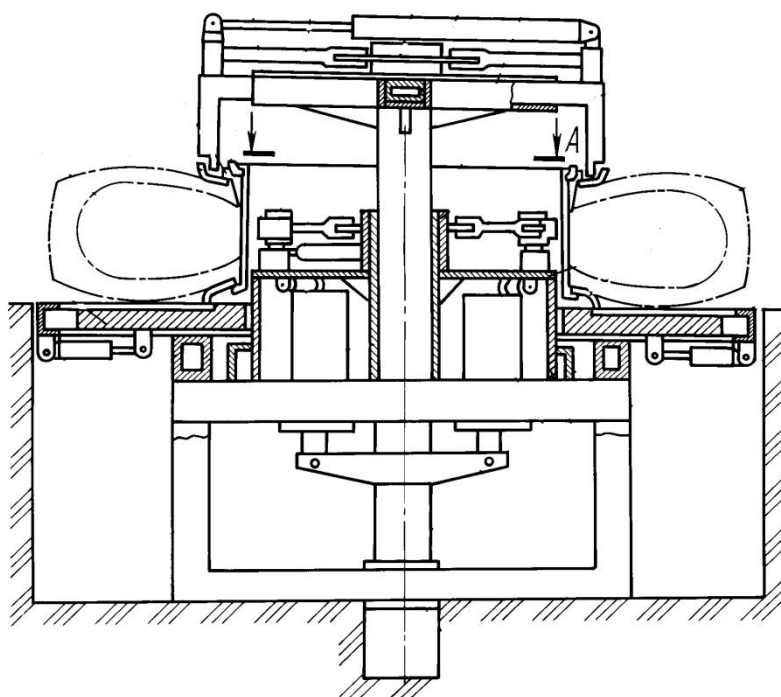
Стенд для монтажа и демонтажа шин
